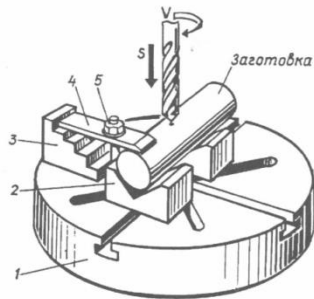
Схема застосування прихоплювача зі східчастою опорою: 1 – планшайба; 2 – призма; 3 – опора; 4 – прихоплювач; 5 – гайка
